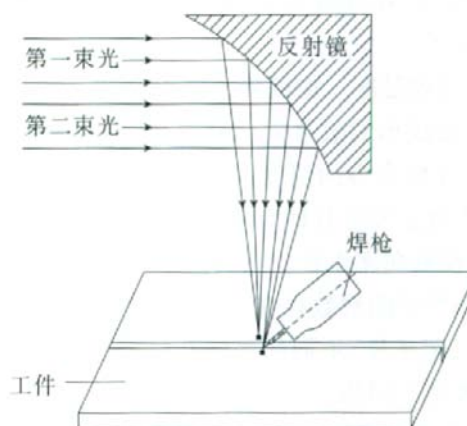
双焦点激光-TIG 电弧复合焊接装置
